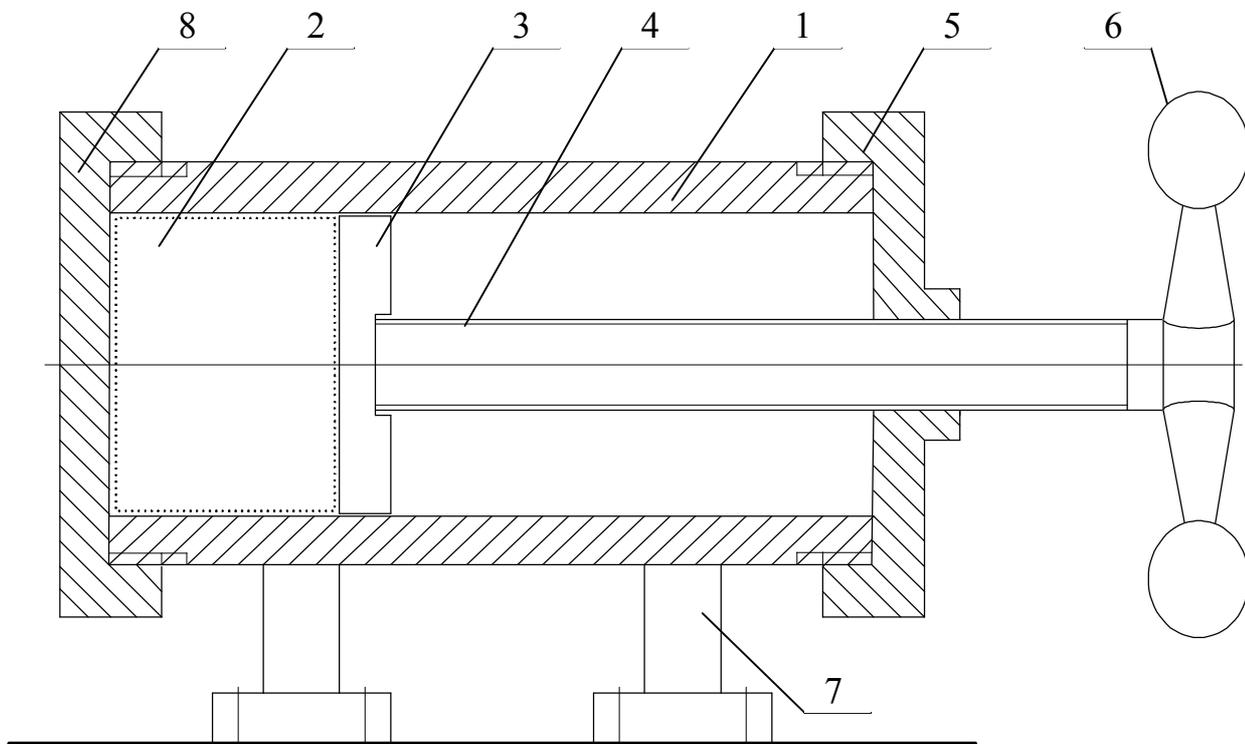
Схема установки для pelletирования: 1 – материальный цилиндр; 2 – исходная смесь для pelletирования; 3 – поршень; 4 – шток с винтовой нарезкой; 5 – задняя крышка; 6 – рукоятка; 7 – съемные опоры; 8 – передняя крышка
